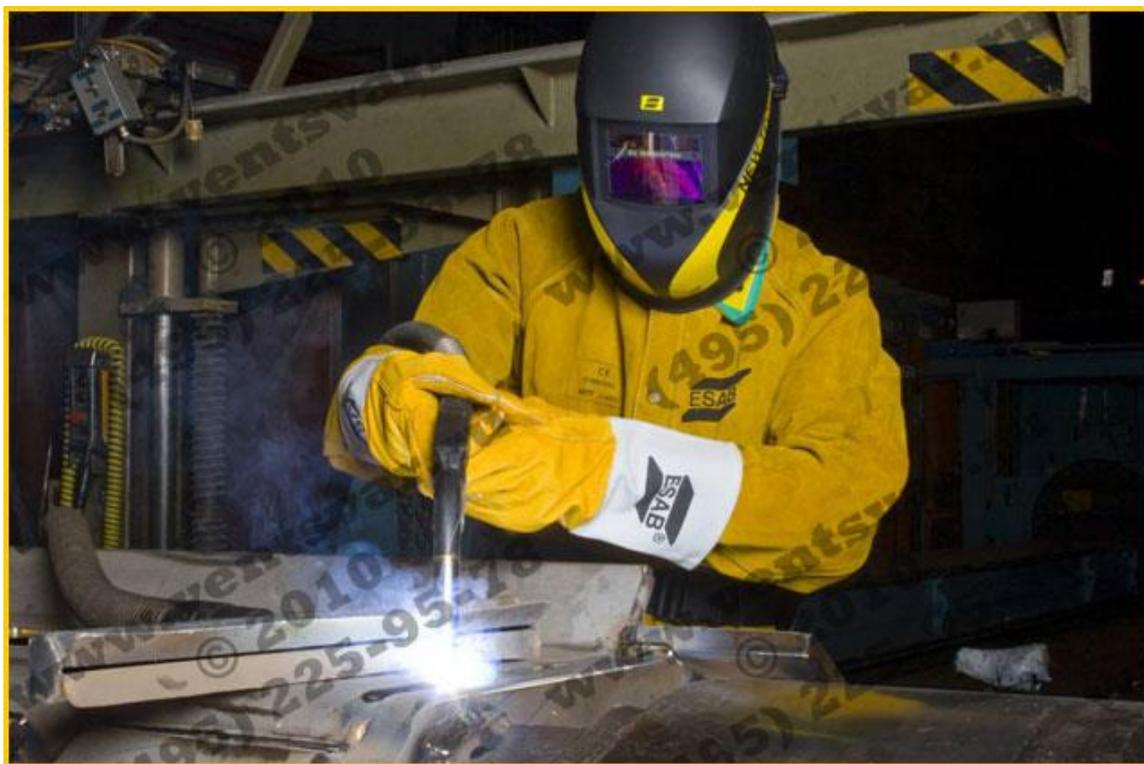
Наплавка открытой дугой порошковой проволокой
